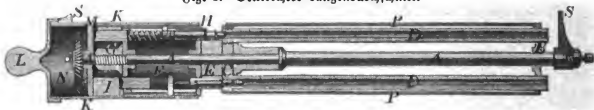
Ansicht von oben mit Horizontaldurchschnitt des hinteren Theiles, ohne Laderichter.
